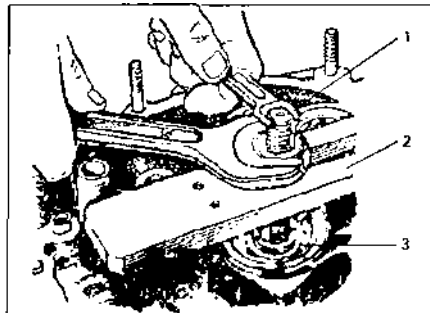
Выпрессовка роликового подшипника шестерни-вала главной передачи:
